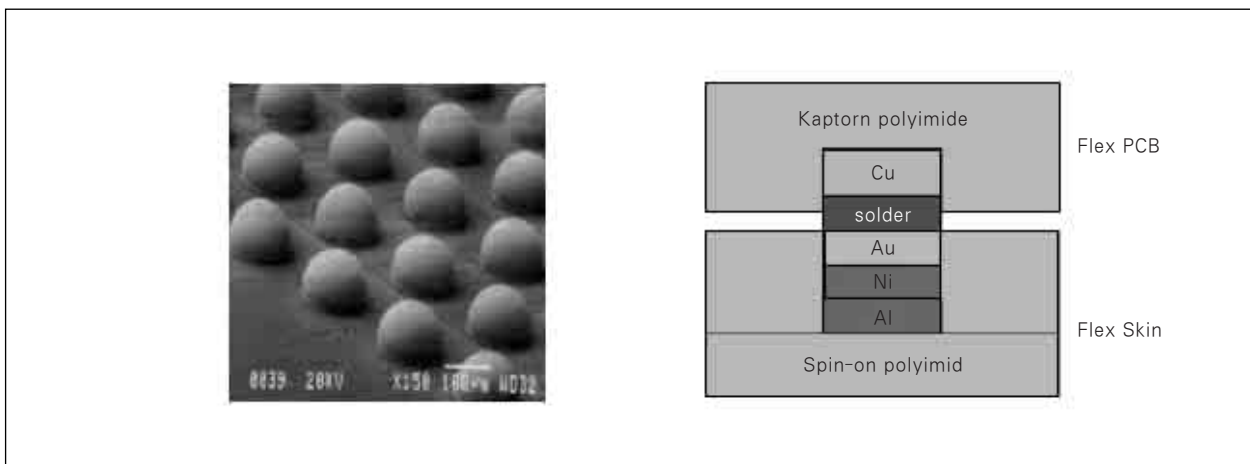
Solder ball을 이용한 유기 기판 간의 CSP의 실현(Coronos Integrated Microsystem, CalTech & UCLA)
